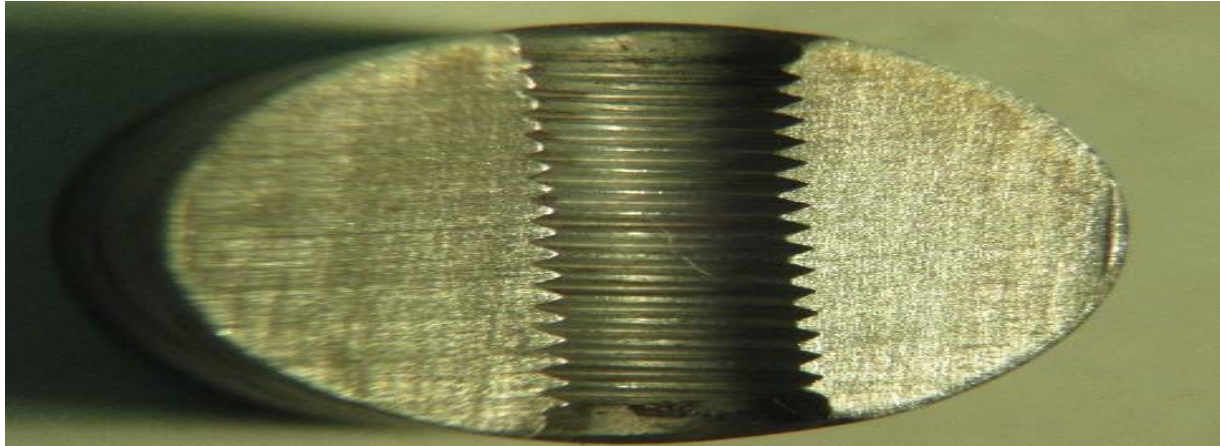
Половинка пресс-формы для изготовления шпильки М4
